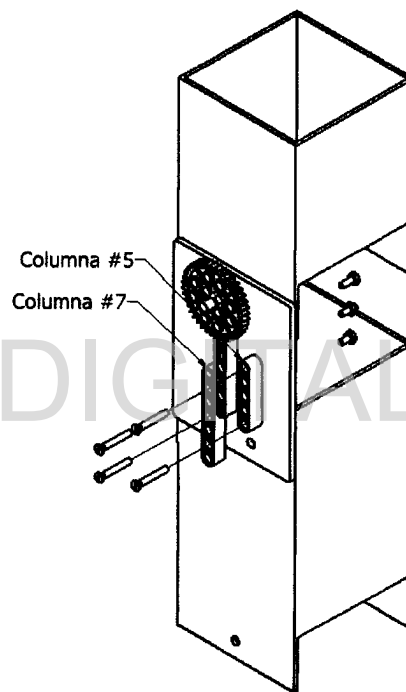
Unión columnas LEGO #5 y #7 al eslabón dos
